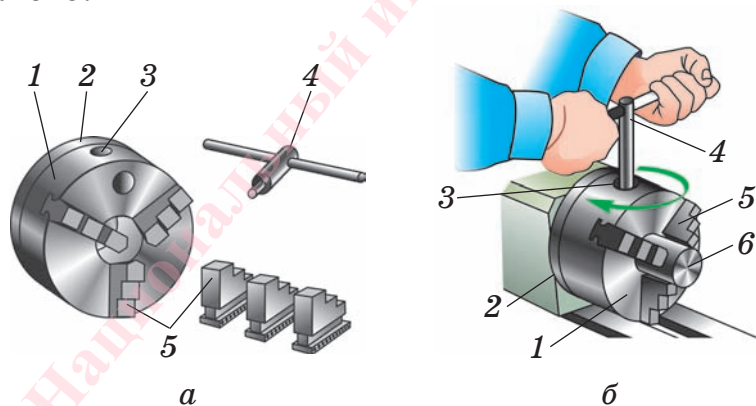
Установка и закрепление заготовки в трехкулачковом патроне:
